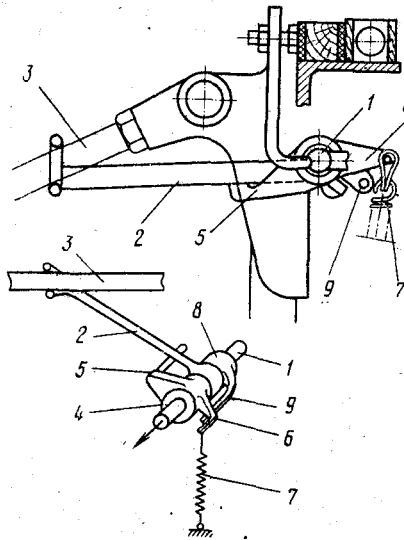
Схема механизма разгрузки клапанов станка АТ-100-5М
